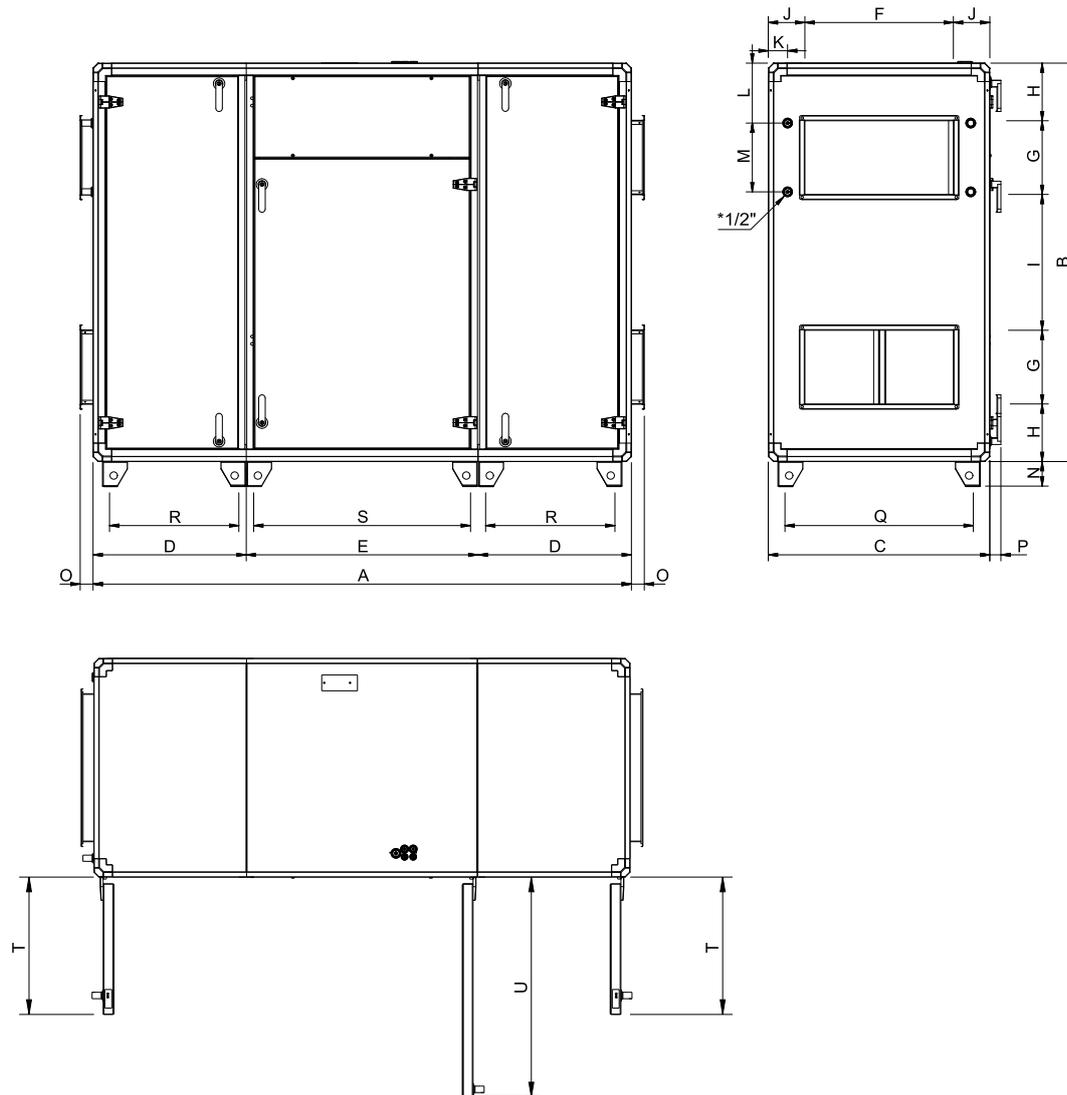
Dimensions (mm) SC03-SC04 (version gauche)
